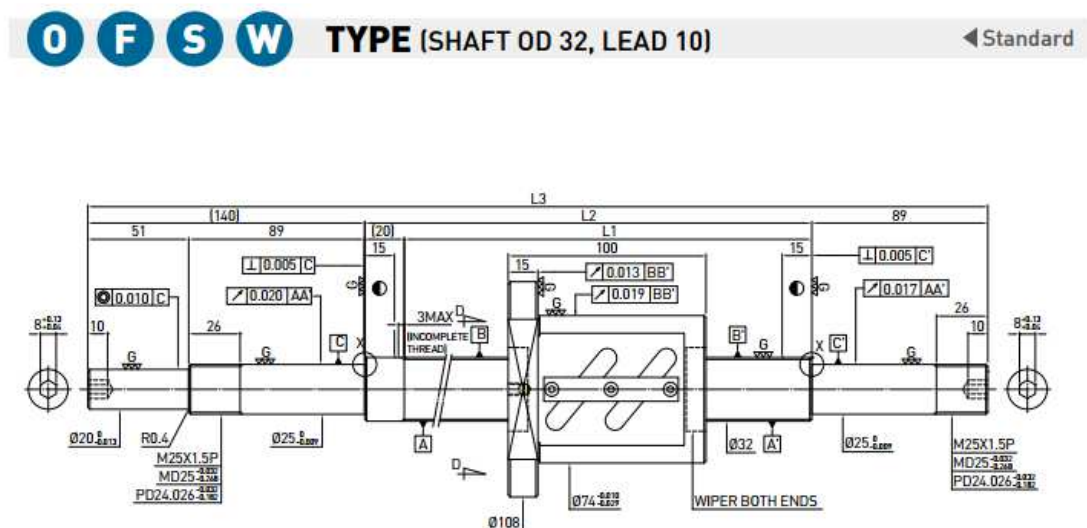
Tornillo de bolas OFSW diámetro 32mm, paso 10mm
